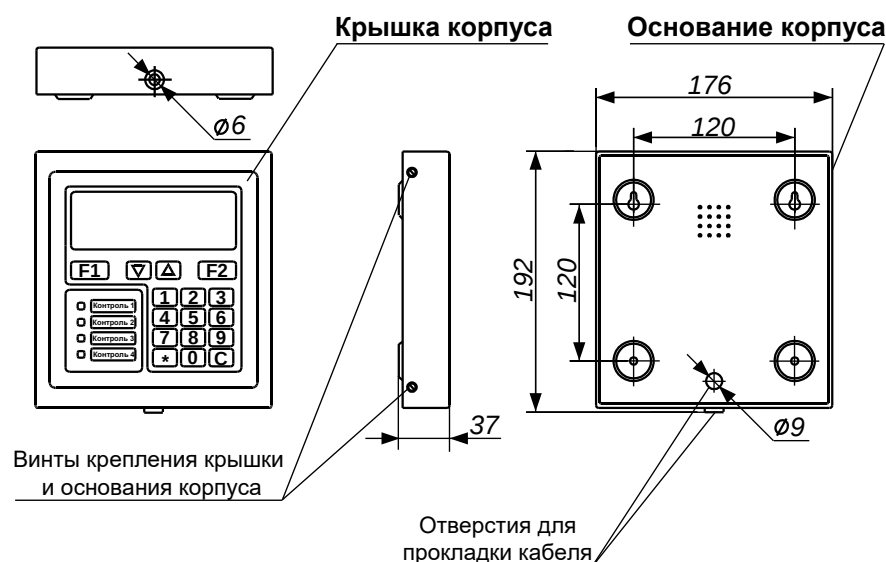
Габаритные и присоединительные размеры (накладное исполнение)
